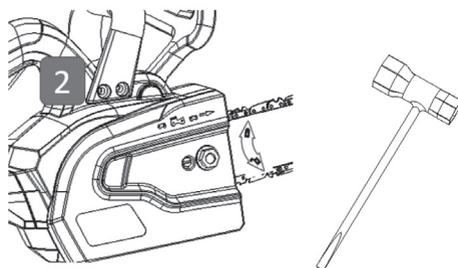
Tournez la vis du tendeur de chaîne dans le sens des aiguilles d'une montre pour amener le guide-chaîne aussi près que possible de la roue à chaîne.
